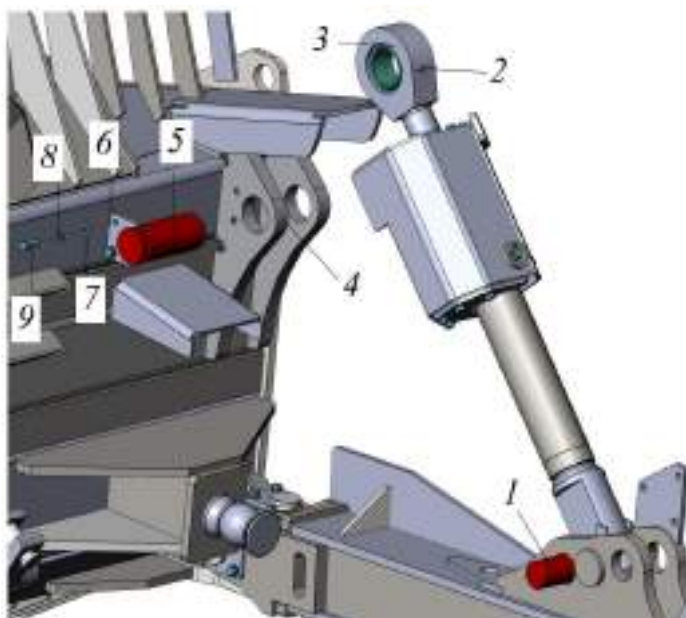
Крепление гидроцилиндра перекоса к зеркалу
